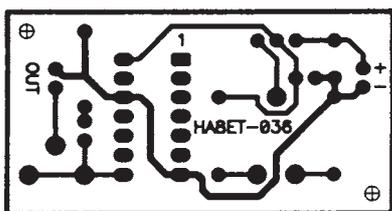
Zapojení oscilátoru podle HA8ET - 036
